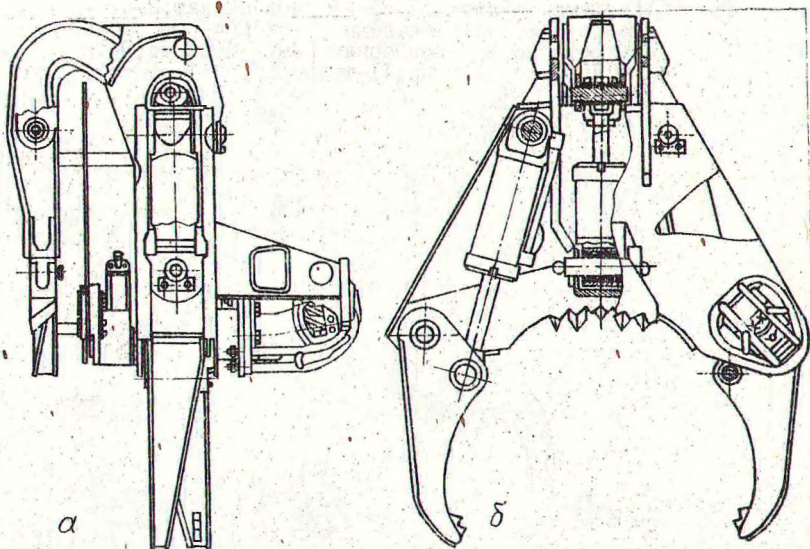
Захватно-срезающая головка ВПМ: а-вид сбоку; б-вид сверху.
